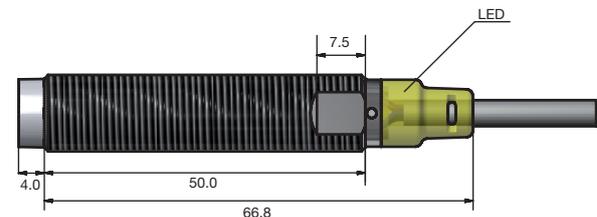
Lange Ausführung, Nicht bündiger Einbau, Kabel
